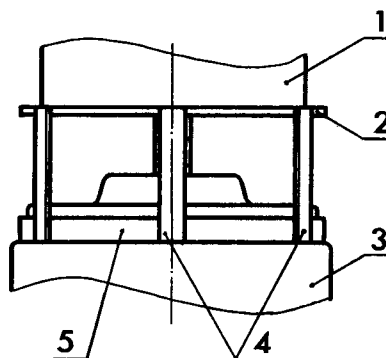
Схема изготовления кожуха сцепления: 1 — коробка передач, 2 — диск, 3 — двигатель, 4 — планки, 5 — обрuch.
